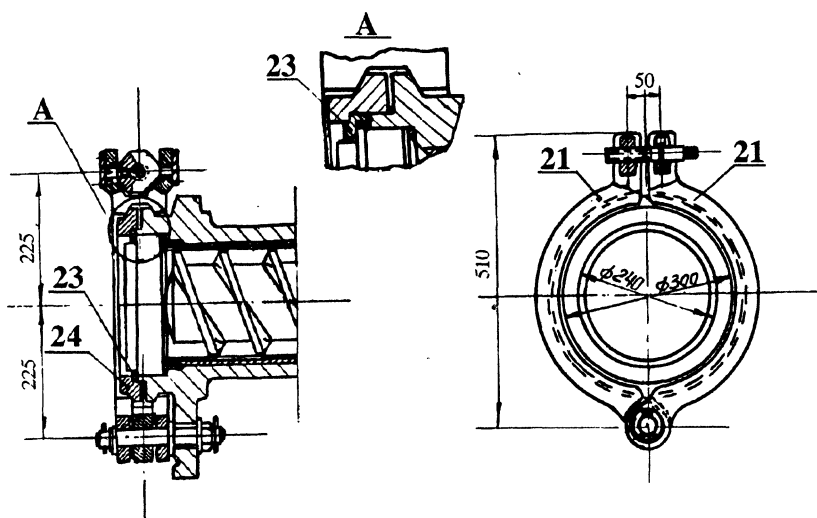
Крепление матричной обоймы пресса Ш-2В.
